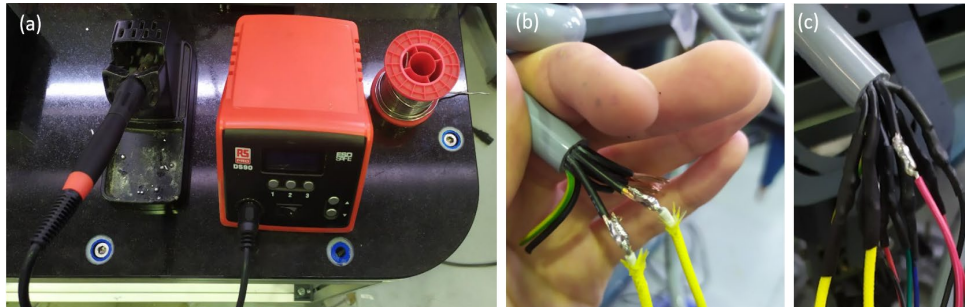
Fotografía de (a) soldador y cable de estaño empleados para empalmar los cables, (b) cables empalmados mediante soldadura de estaño y (c) soldaduras aisladas con el tubo termorretráctil.
